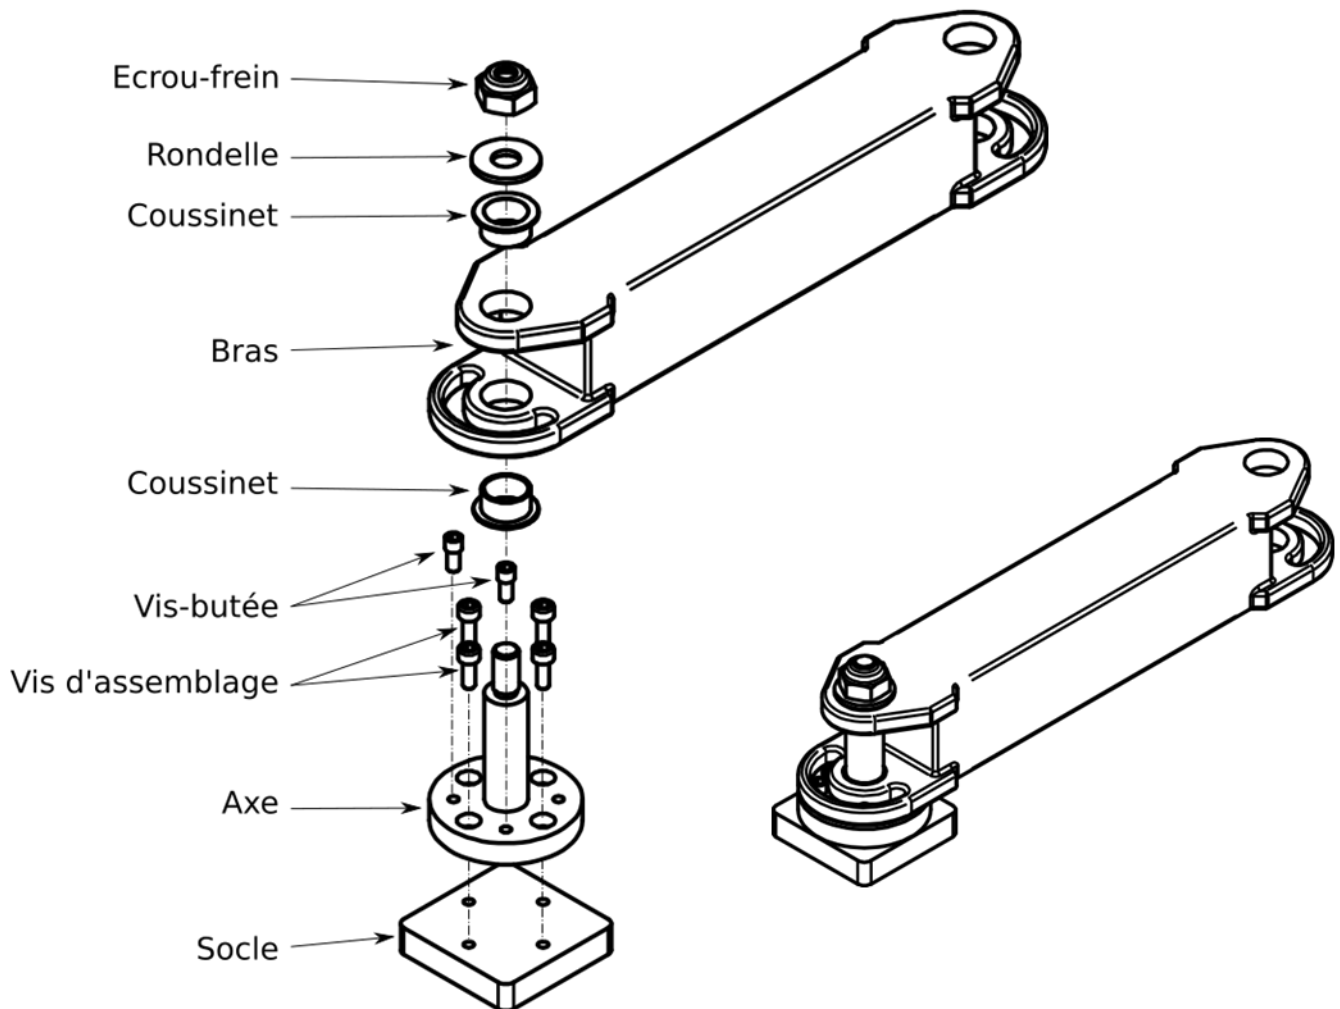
Vue en éclatée et en perspective de l'assemblage.
